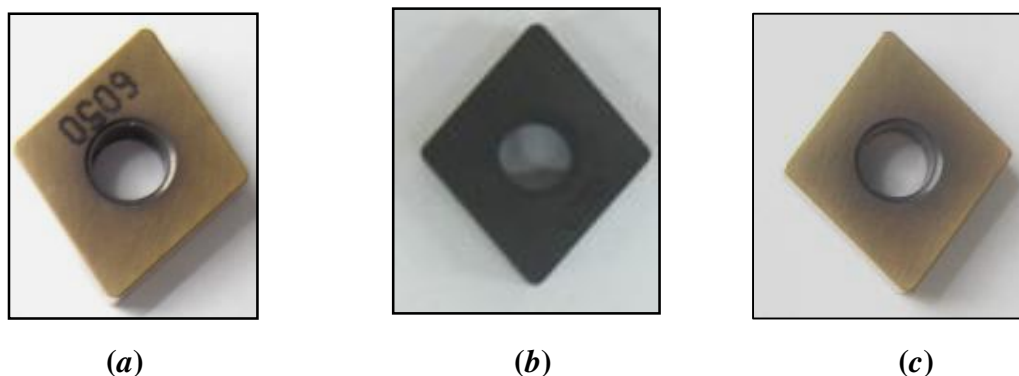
Vue d'ensemble des plaquettes céramiques CNGA 12 04 08
